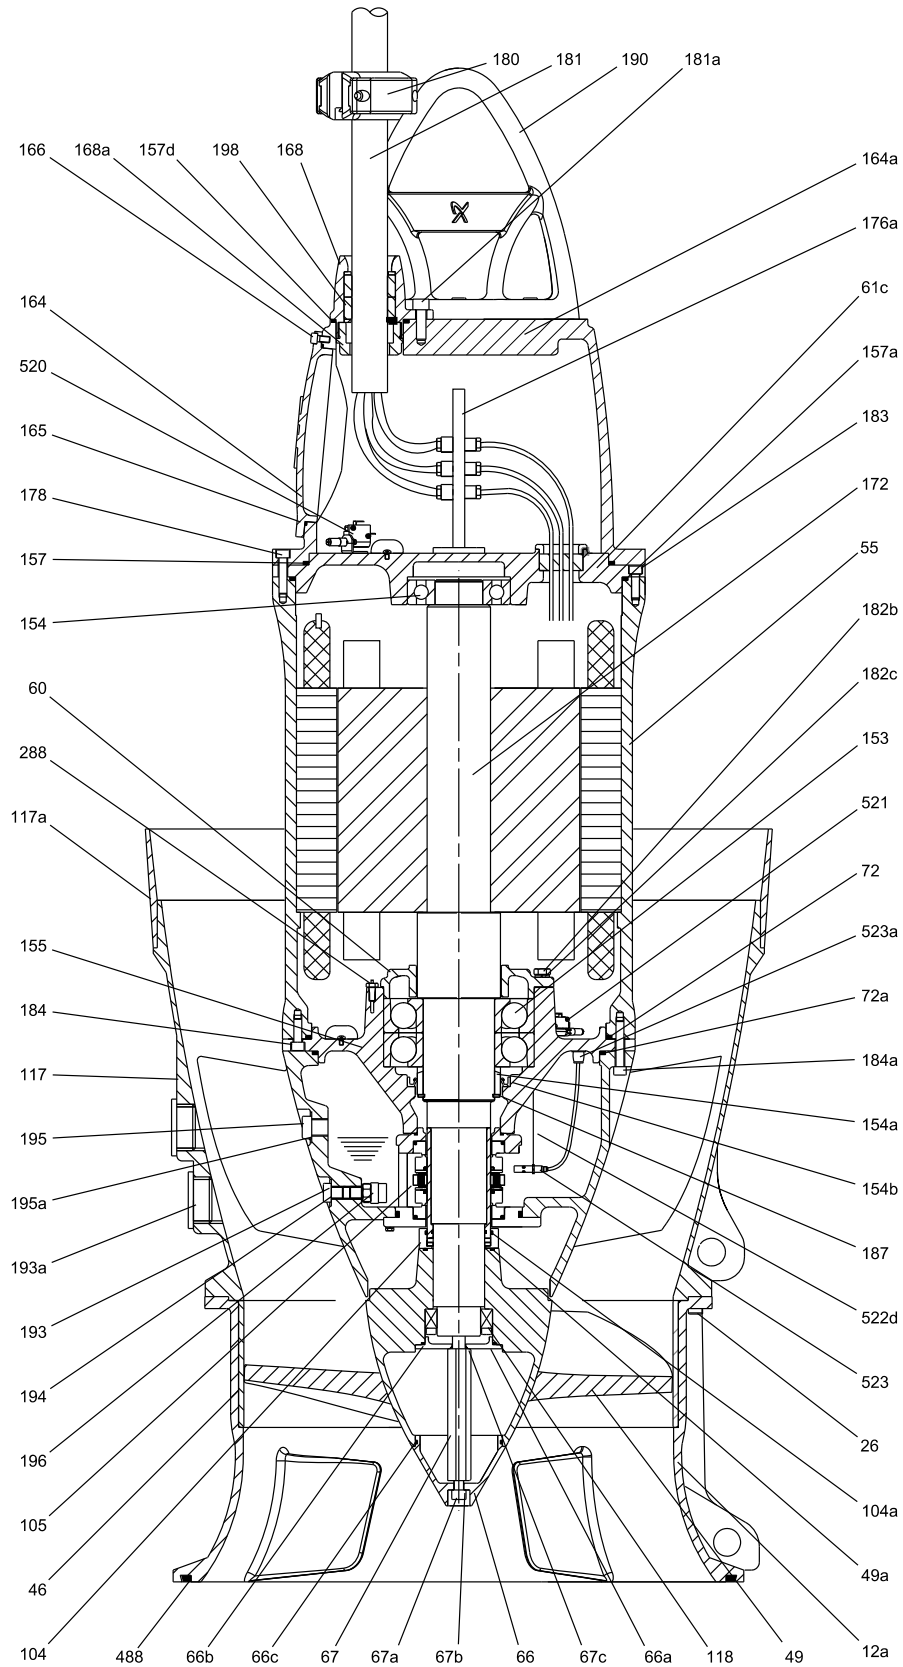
Чертеж в разрезе, KPL, обсадная труба диаметром 650-1800
